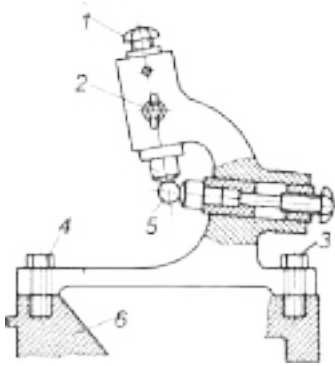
Елементи рухомого люнета: 1, 2, 3, 4 — гвинти; 5 — заготовка; 6 — супорт
